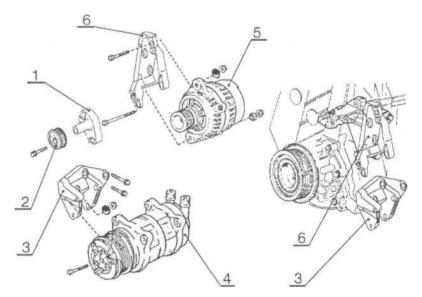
Монтаж элементов климатической установки на двигатель: 1 - кронштейн натяжителя; 2 - ролик натяжной; 3 - кронштейн подушки штанги подвески двигателя; 4 - компрессор; 5 - генератор; 6 - кронштейн генератора.
